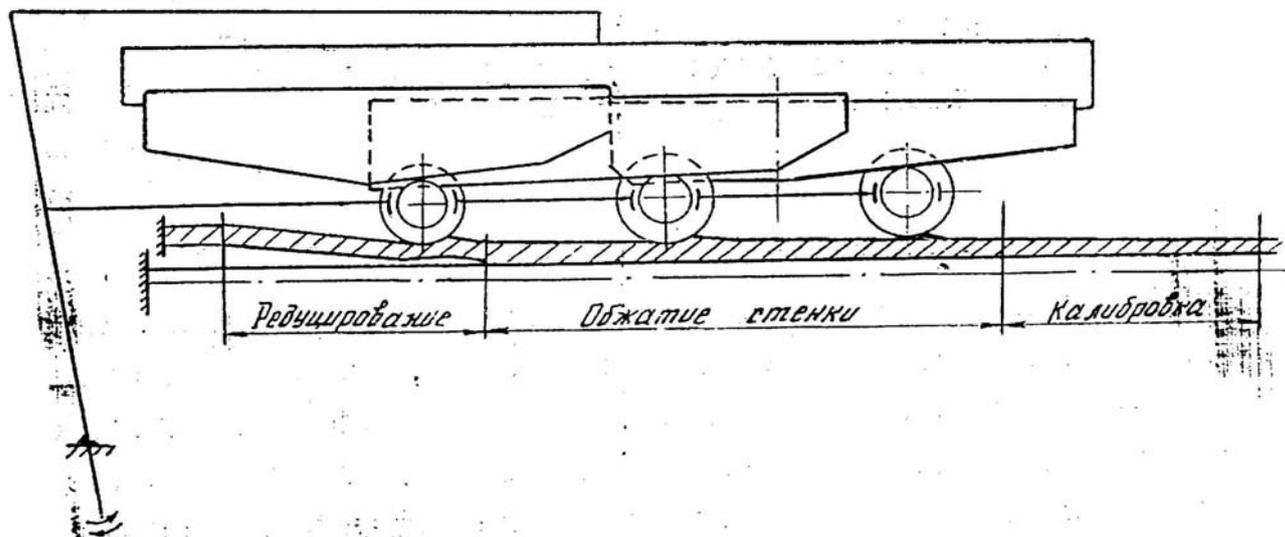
Процесс непрерывной периодической трехрядной роликовой прокатки.
